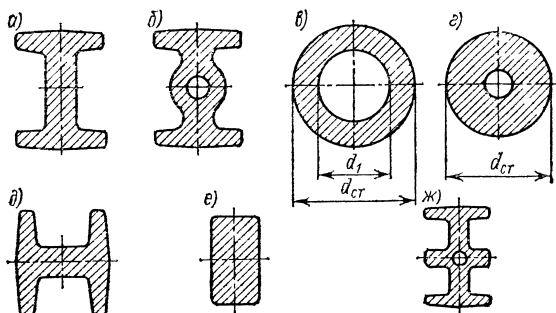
Формы поперечных сечений стержня шатуна: а — двутавровое; б, ж — усложненные двутавровые; в, г — круглые; д — Н-образное; е — прямоугольное
